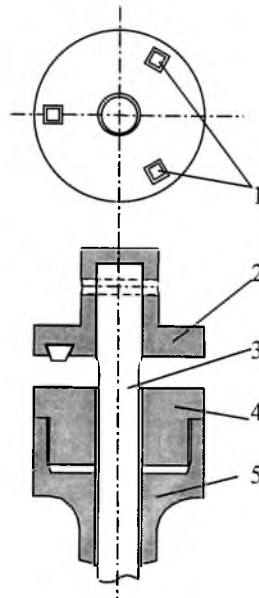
Схема образцов для проведения адгезионных испытаний алмазов с металлом: 1 – алмазы; 2 – образец-державка; 3 – графитовый стержень; 4 – металлический образец; 5 – графитовая труба.
